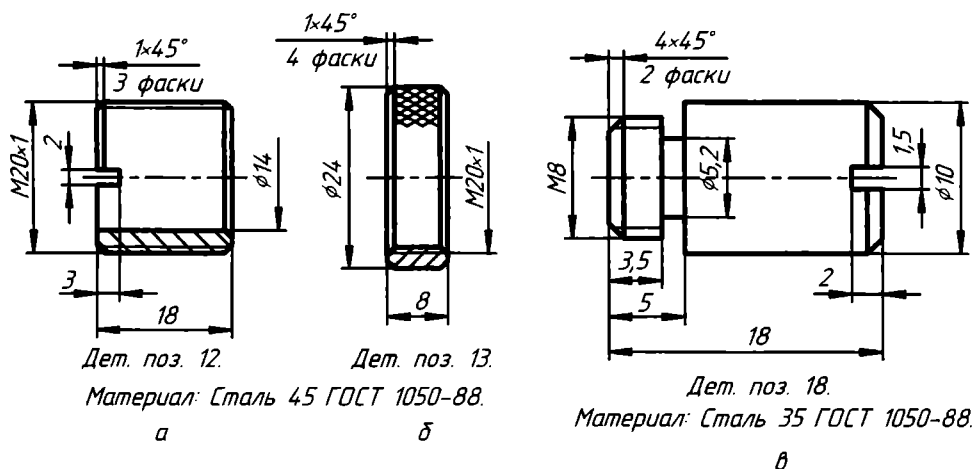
Чертежи: а — втулки; б — гайки; в — пальца
